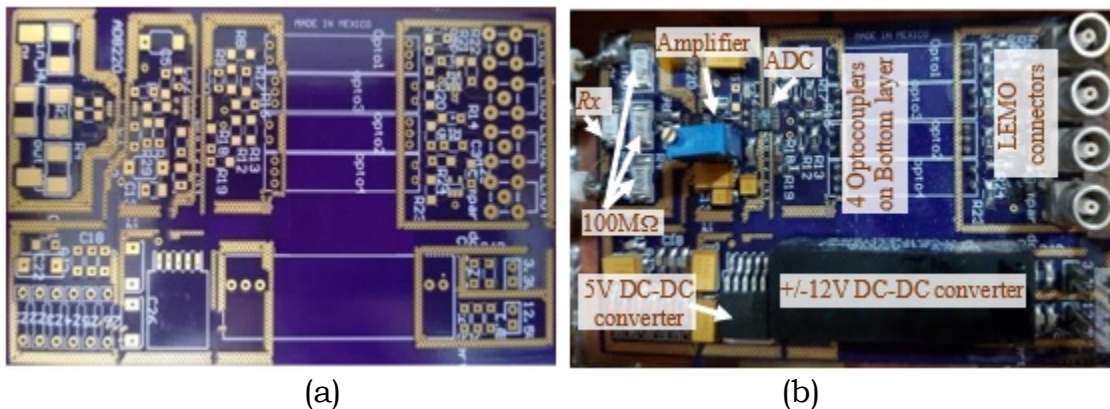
Foto de la PCB. (a) PCB sin componentes and (b) PCB con componentes.
